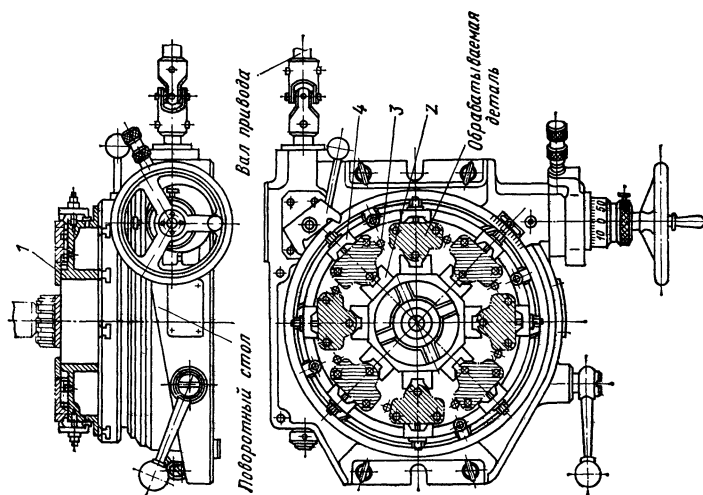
Наладка на круглый поворотный стол для обработки плоскостей деталей сложного контура методом непрерывного фрезерования
